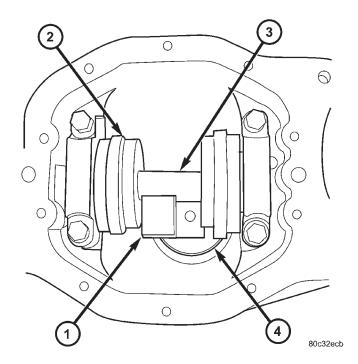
HERRAMIENTAS DE PROFUNDIDAD EN EL CARTER
